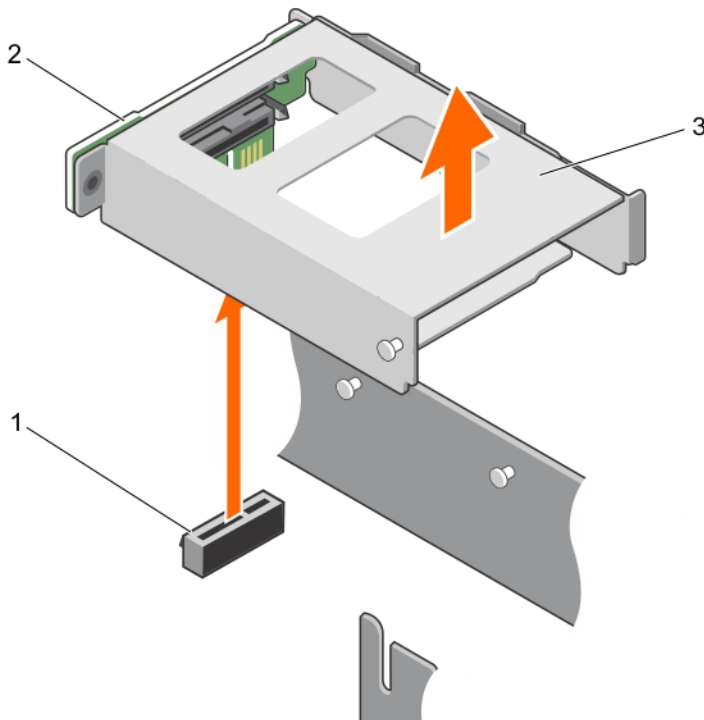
Retrait du bâti de lecteur SSD de 1,8 pouce
